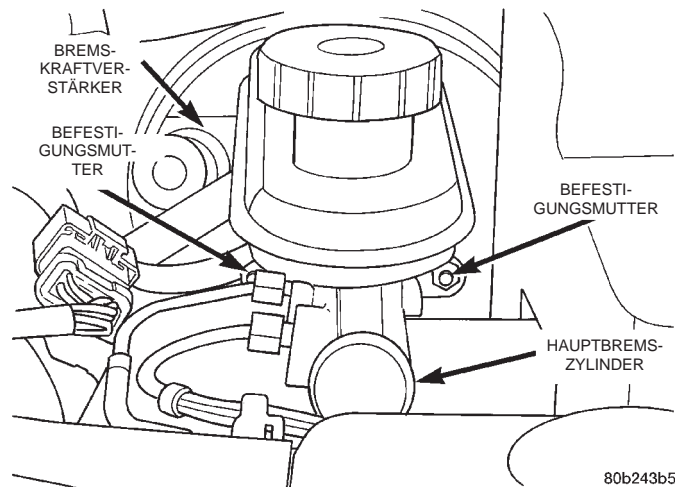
Befestigung des Hauptbremszylinders am Bremskraftverstärker
